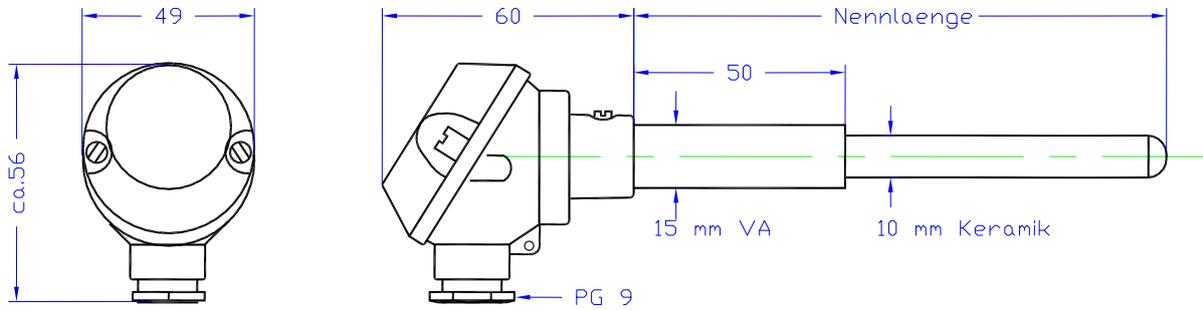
Thermoelement mit Kopf LK (geschlossen mit Stülpdeckel)
